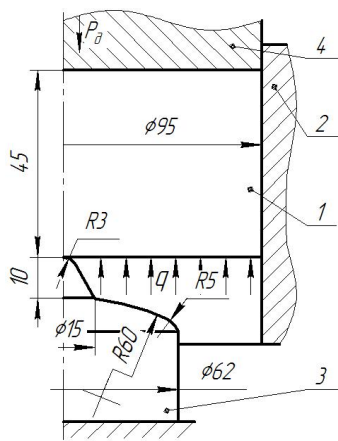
Розрахункова схема видавлювання порожнини матриці в умовах дії протитиску на вільну поверхню заготовки
